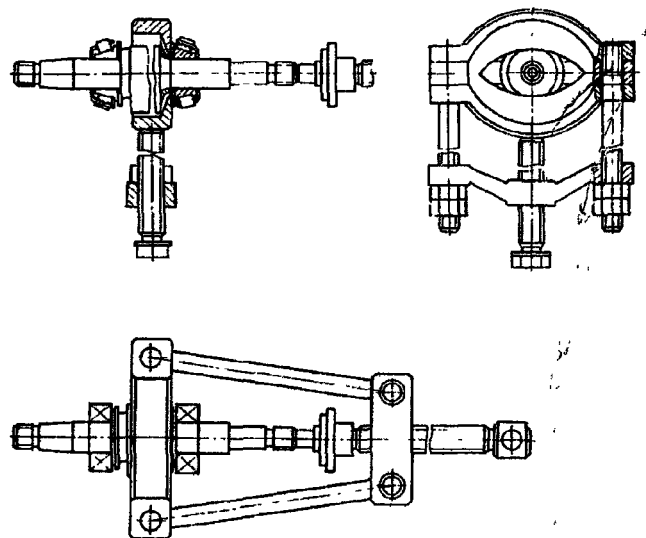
Снятие подшипников кулачкового вала ТНВД
